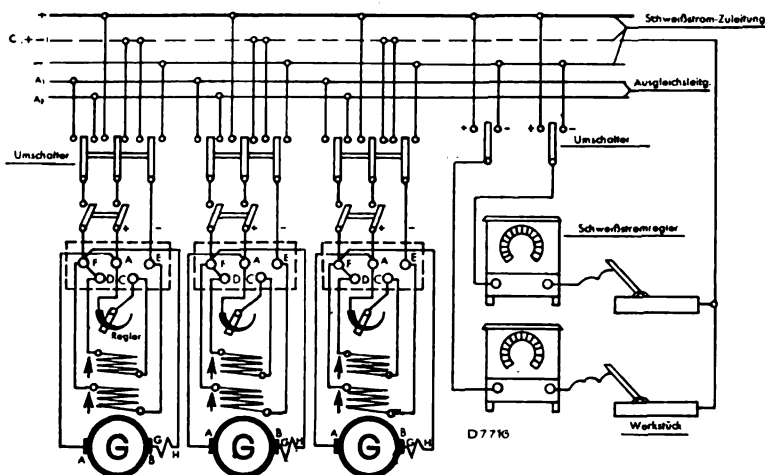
Grundschriftplan des Schweißnetzes einer Vielstellenschweißanlage für das Schweißen mit verschiedener Polarität.
